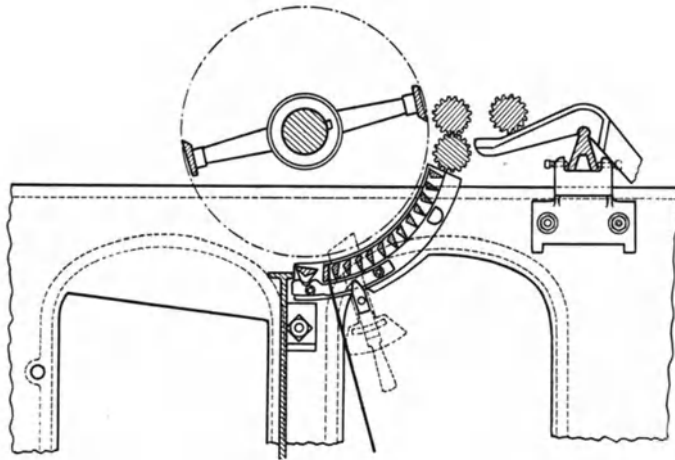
Schläger mit Walzenzuführung (Howard & Bullough Ltd., Accrington).
